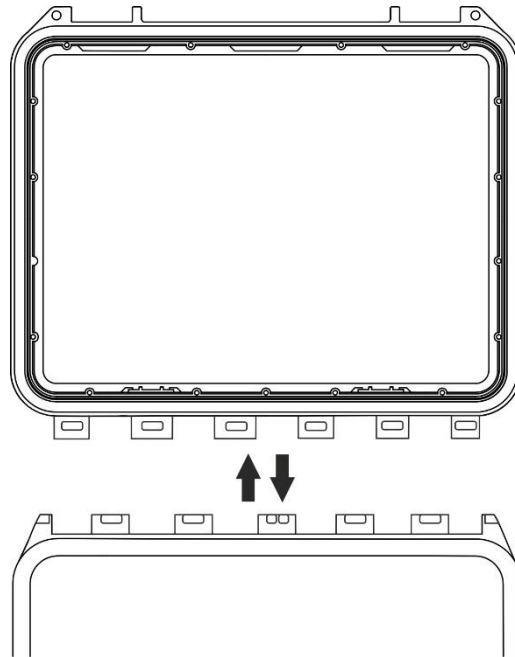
Retirada de la tapa de la maleta del instrumento – Paso 3
